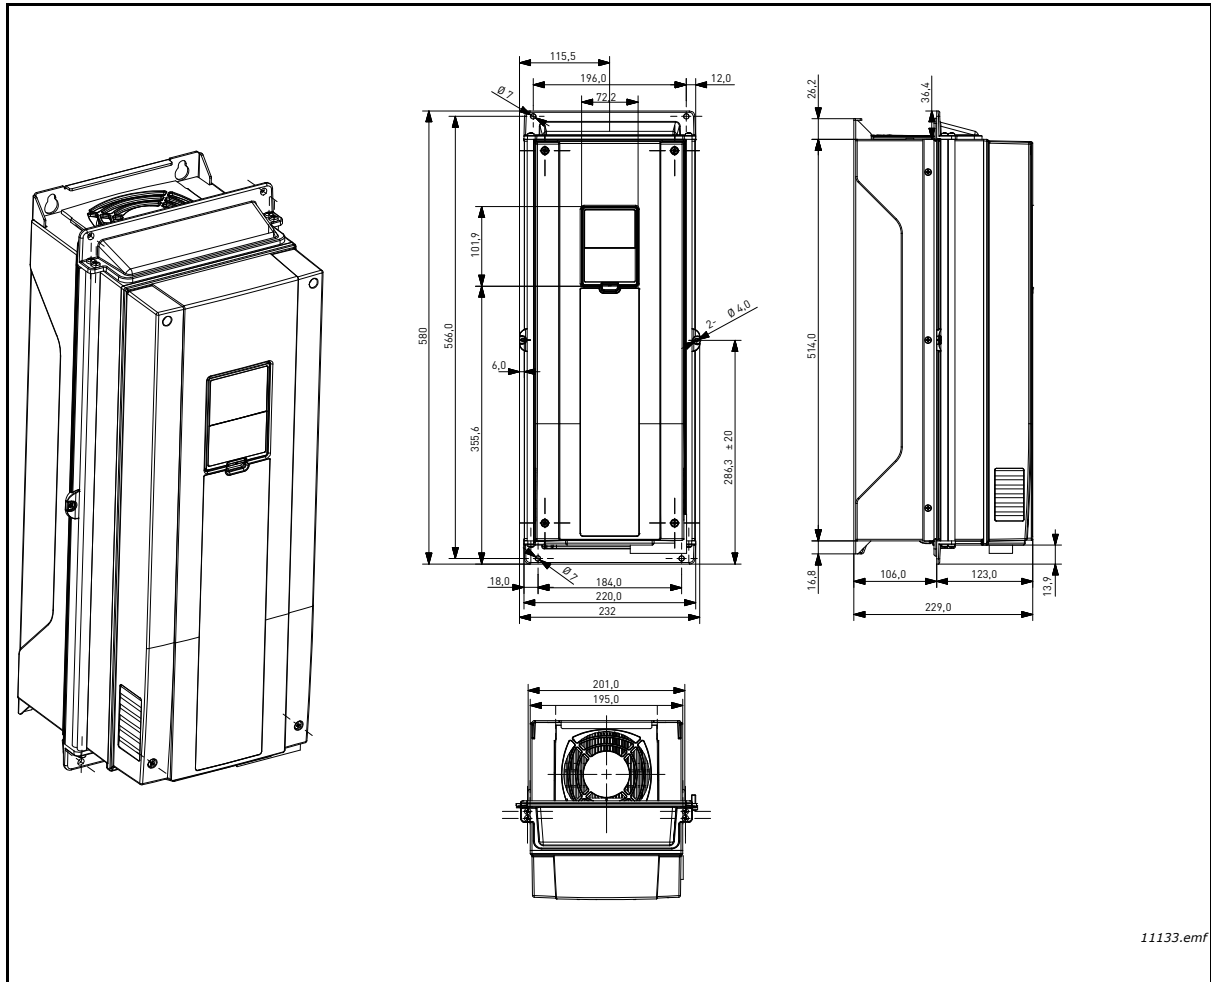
viser dimensionerne af monteringsåbningen, og Figur 11. - 16. viser dimensionerne af frekvensomformerne med flangemonteringsindstillingen.
